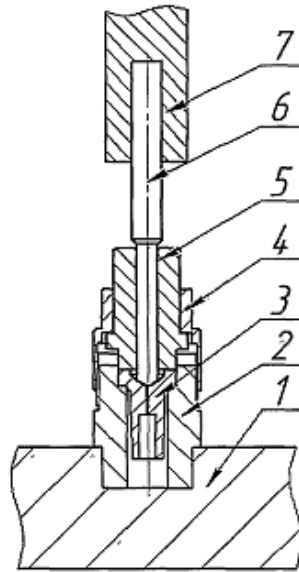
Оснащення для відновлення запірних клапанів ЕГФ типу CR фірми Bosch: 1 – упорна плита; 2 – корпус; 3 – сідло клапана ЕГФ; 4 – гайка; 5 – направляюча проставка; 6 – притир; 7 – затискний патрон.
